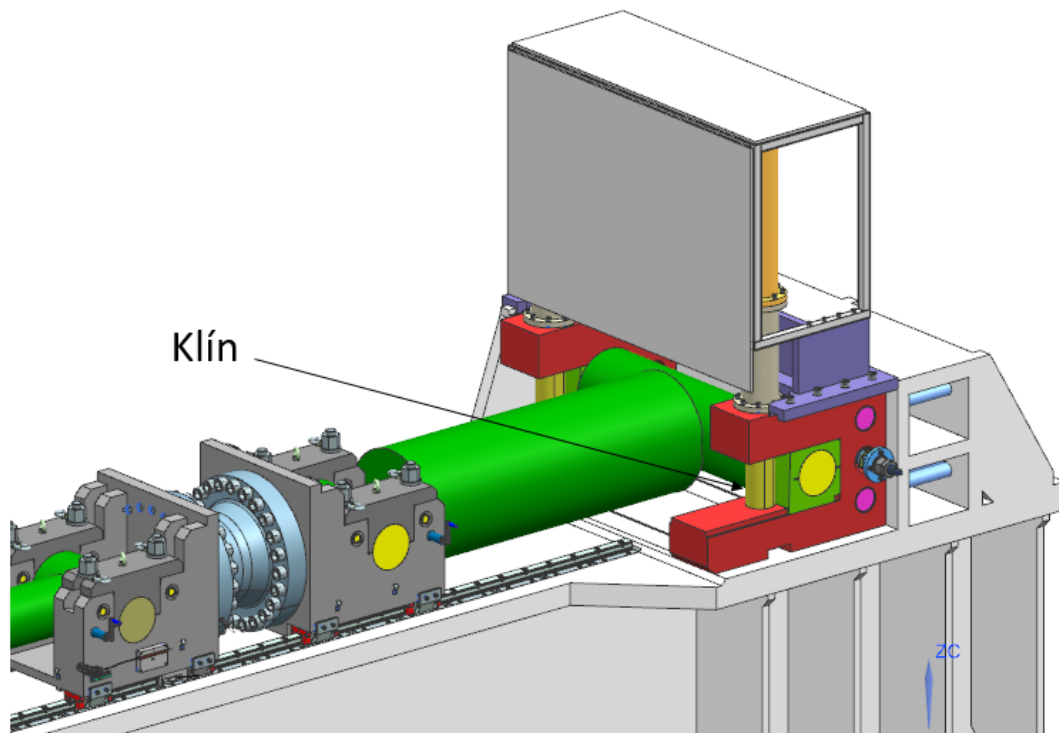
Upevnění testovaného HM – položení hydromotoru
